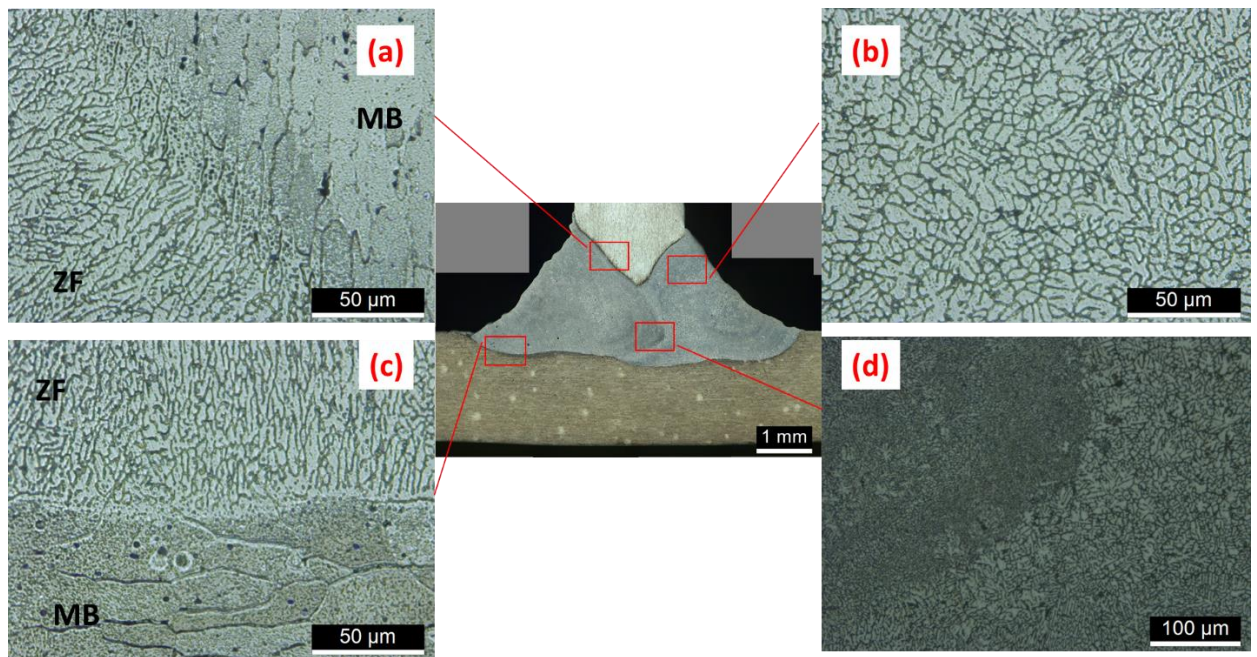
Estrutura da zona fundida de uma soldadura (Amostra 79)
